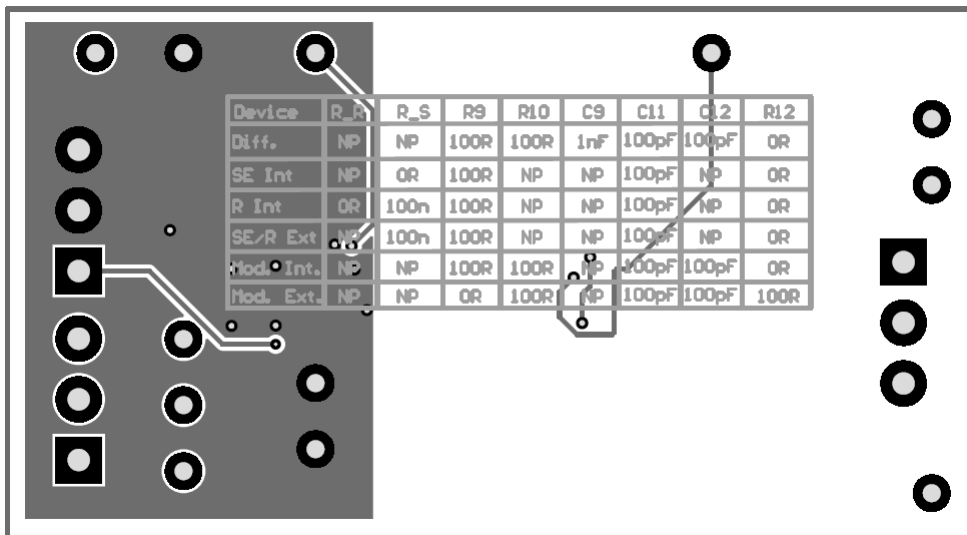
AMC43xxDVVEVM 顶部 PCB 图
